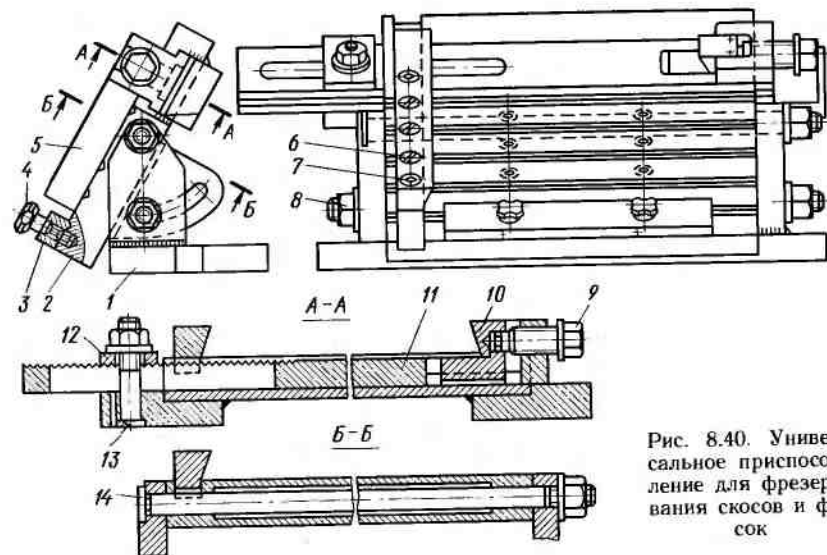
Универсальное приспособление для фрезерования скосов и фасок
